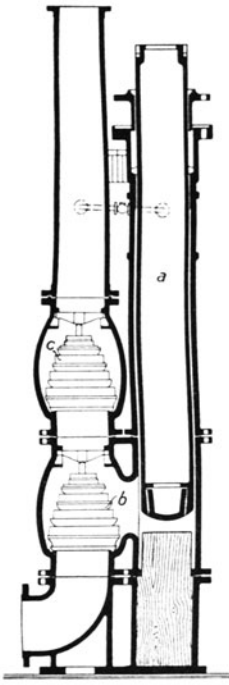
Druckpumpe einer Gestängewasserhaltung.
